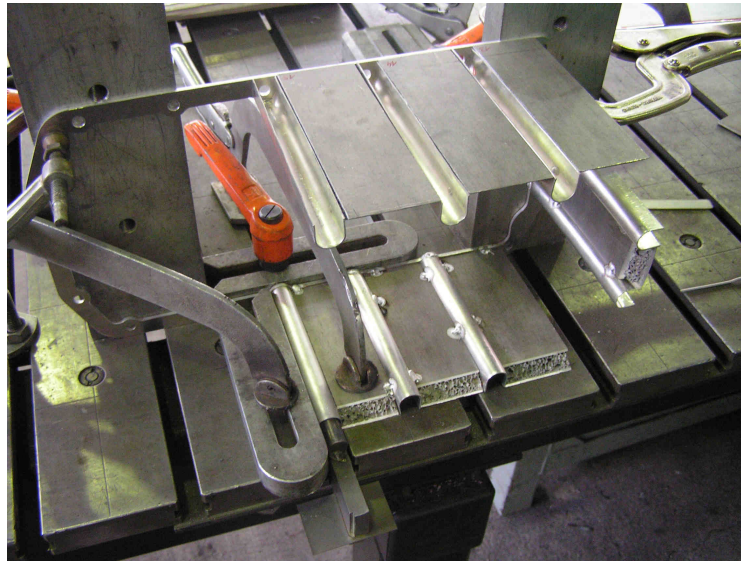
Aufgespannte Baugruppe vor dem Schweißvorgang
